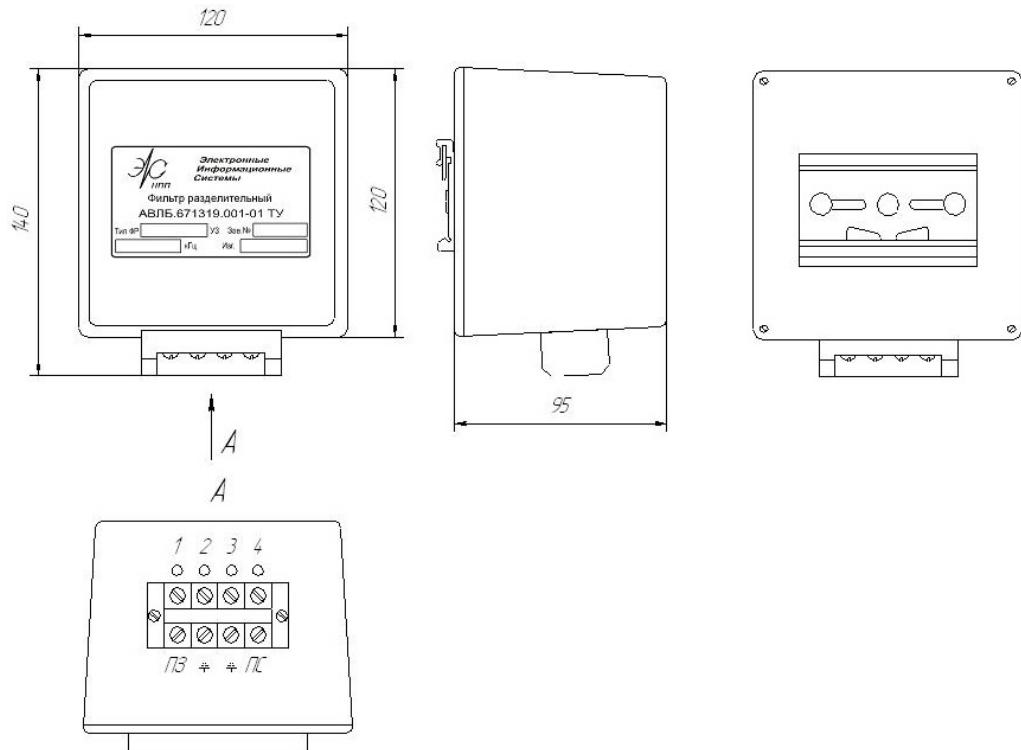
Габаритно-присоединительный чертеж фильтра присоединения ФП.
